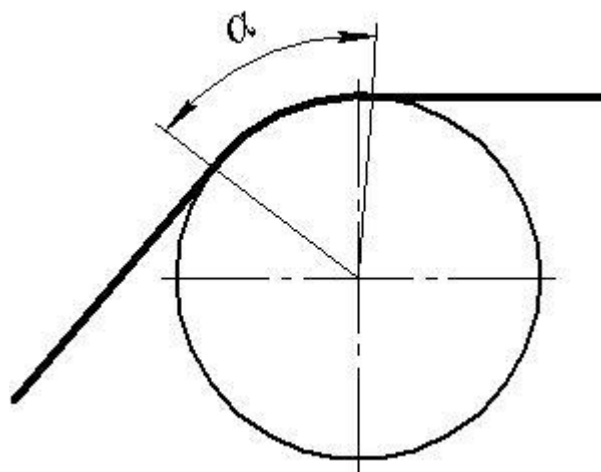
Форма контакта ленты с обрабатываемой деталью
